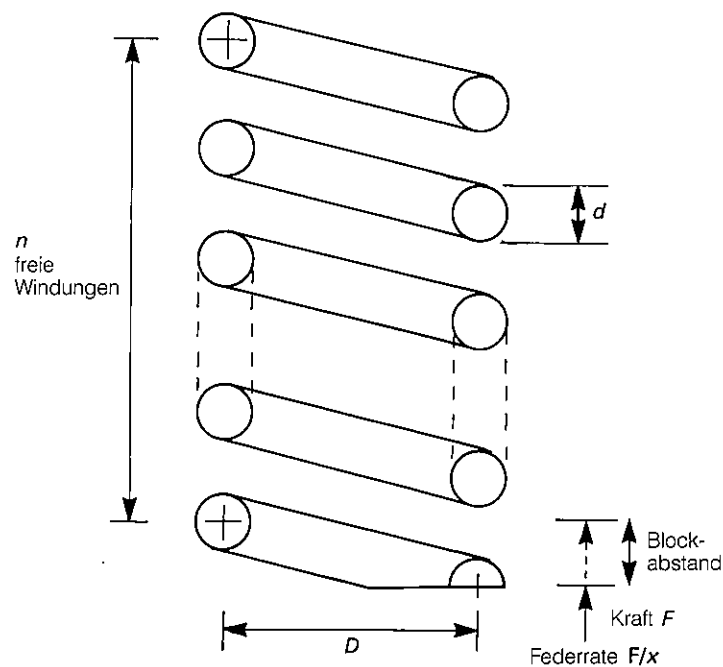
Wichtige Abmessungen einer Schraubenfeder. Die Federrate kann mithilfe dieser Abmessungen berechnet werden.
